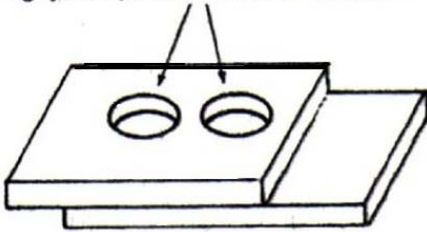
Placas preparadas para soldaduras de tapón
